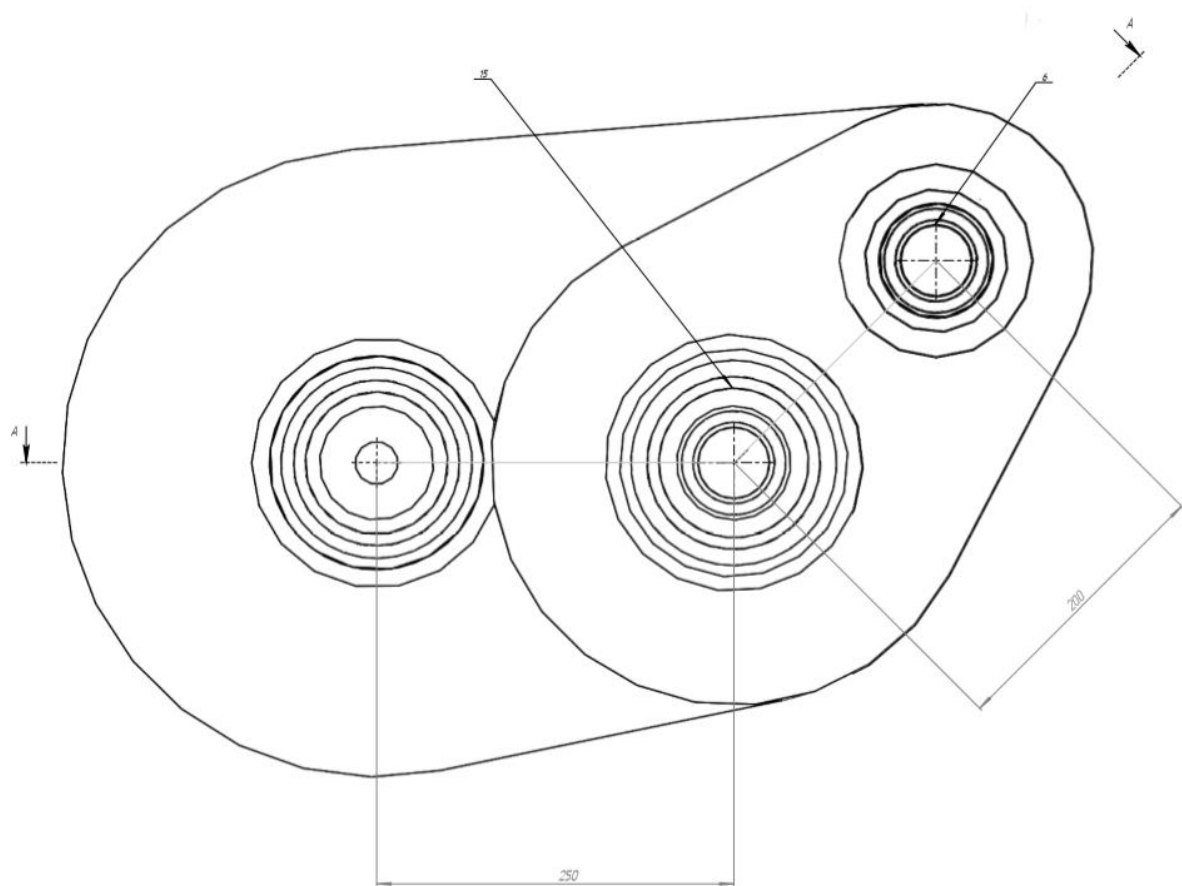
Загальний вигляд заднього редуктора(Вид зліва).
